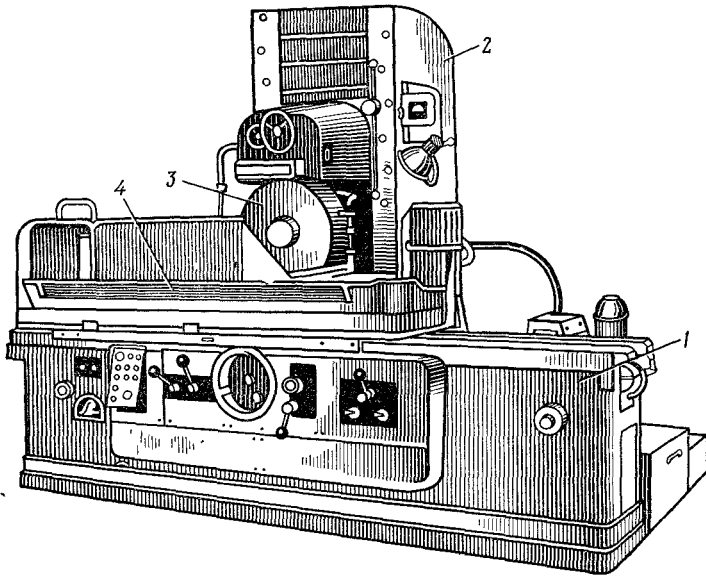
Плоскошлифовальный станок мод. 3Б722
